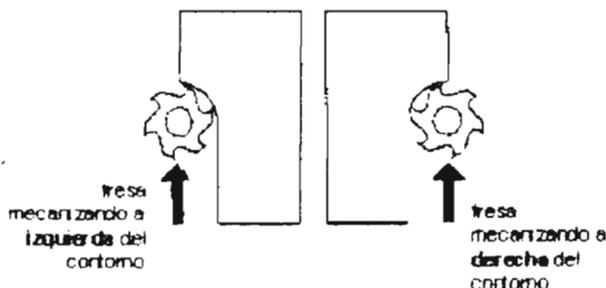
Trayectoria de fresa a izquierda y derecha.
